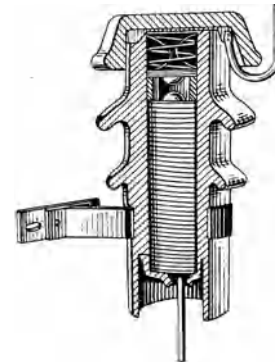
Schnitt durch einen Autovalve-Ableiter. Westinghouse.
